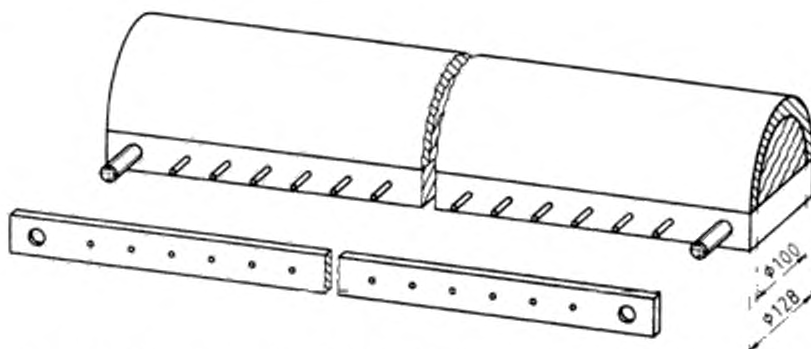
пример опоры калибровочной подкладки и крепежного устройства
